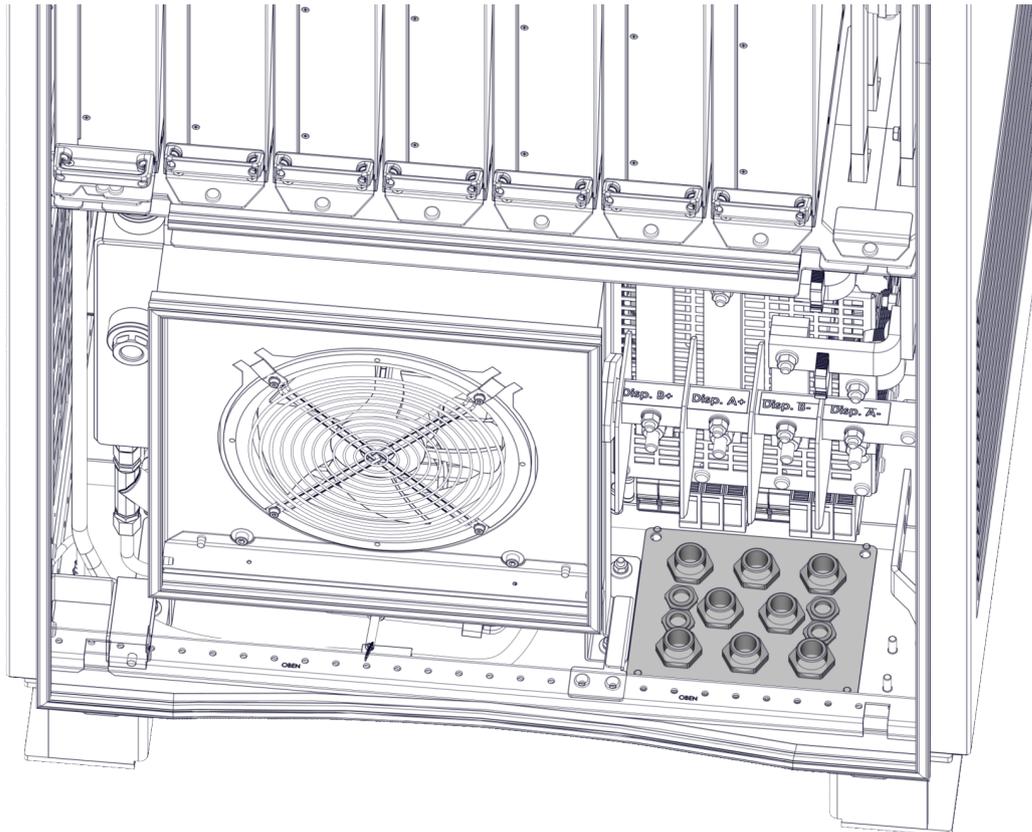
Kabeldurchführungsplatte für die Dispenserkabel
